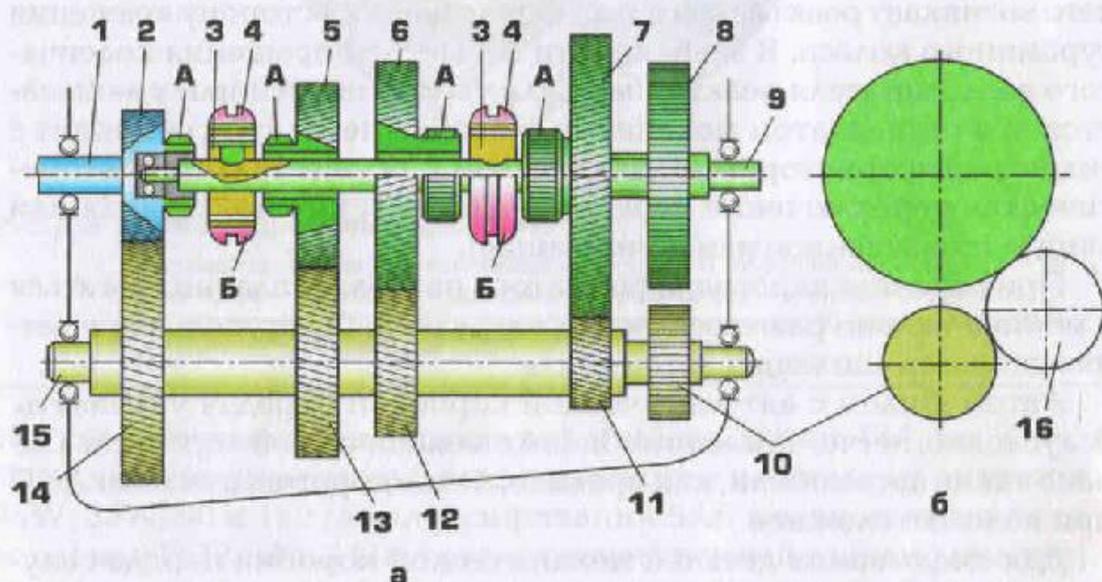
Схема коробки передач с постоянно зацепленными шестернями:
